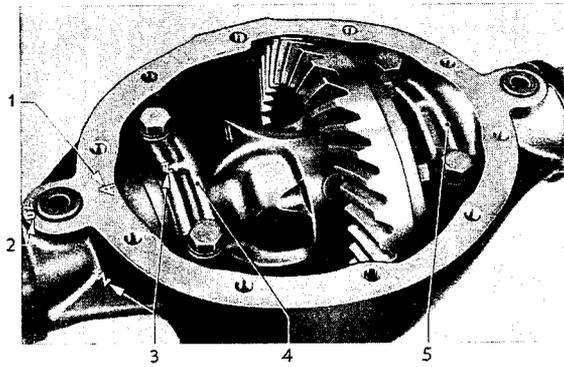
Ausgleichgehäuse mit Tellerrad in Hinterachsgehäuse eingesetzt und mit Lagerdeckeln festgeschraubt
